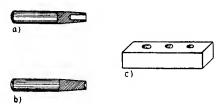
Nietwerkzeuge; Nietzieher (a), Nietkopfsetzer (b) und Gegenhalter (c) zum Einspannen in den Schraubstack
